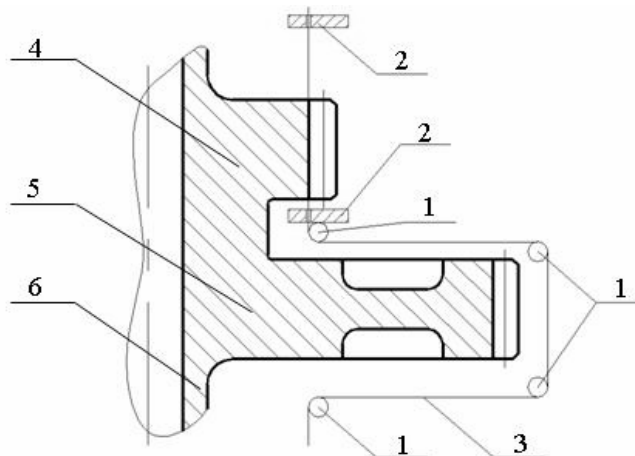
Схема ЭЭО цилиндрического эвольвентного закрытого венца цельного блока зубчатого колеса:
